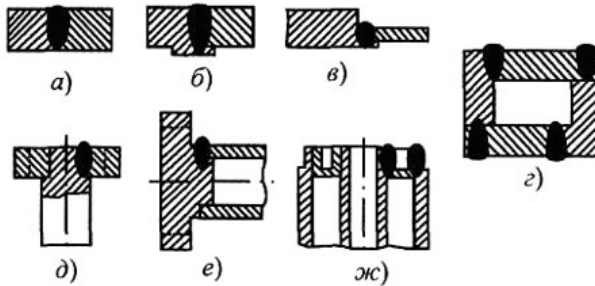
Типы сварных соединений при сварке электронным лучом:
